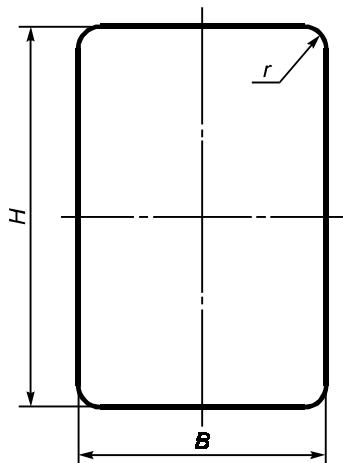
Размеры прямоугольных знаков вертикального формата
